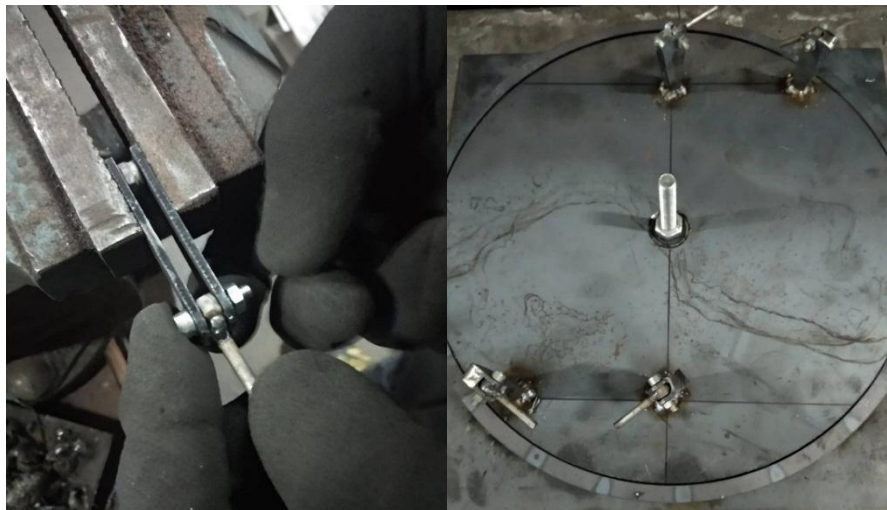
Pormenor da montagem do travamento da cadeira; verificação das medidas e colocação dos componentes
